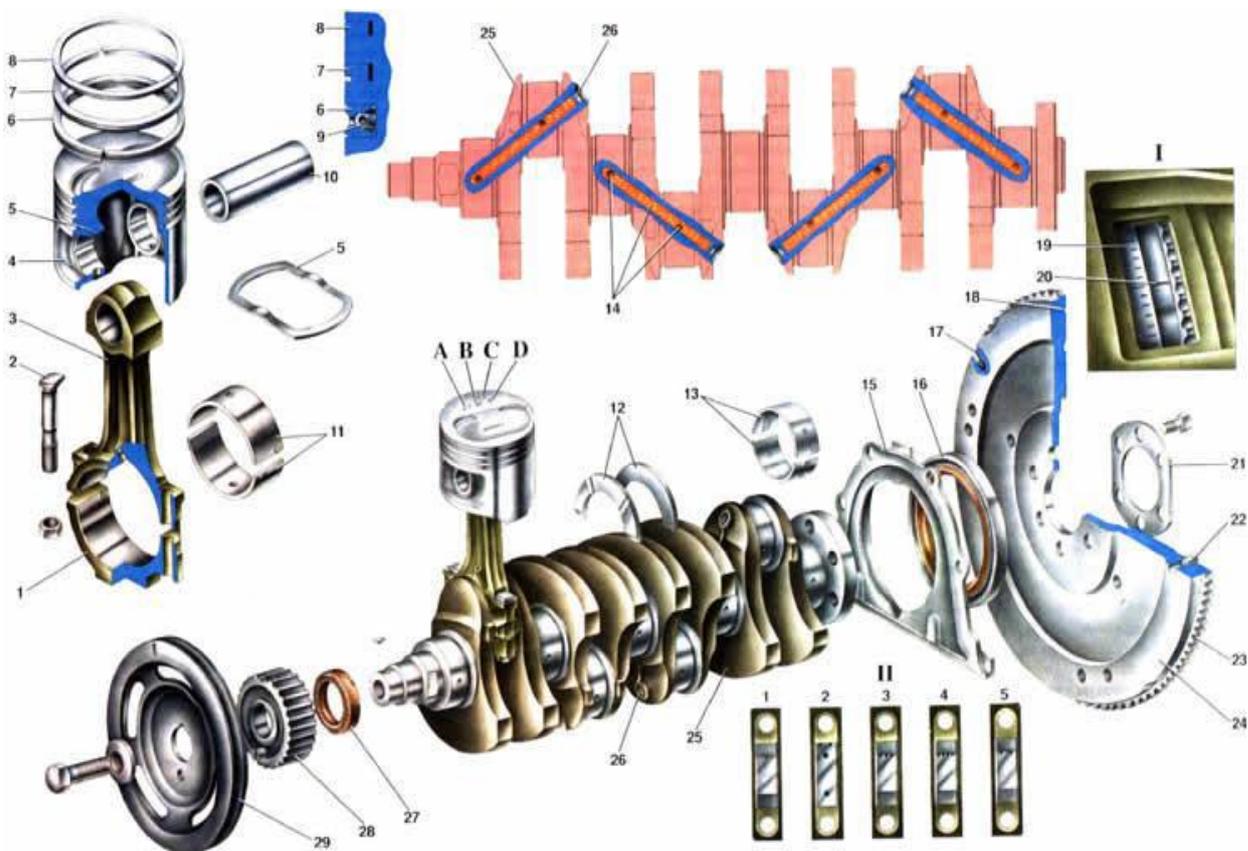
Кривошипно-шатунный механизм карбюраторного двигателя
